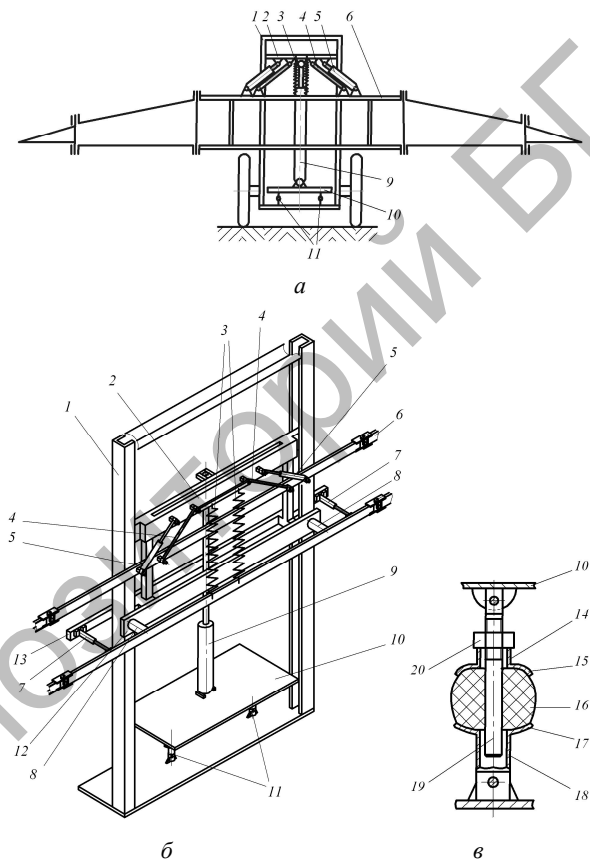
Схема установки штанги на раме полевого штангового опрыскивателя:
